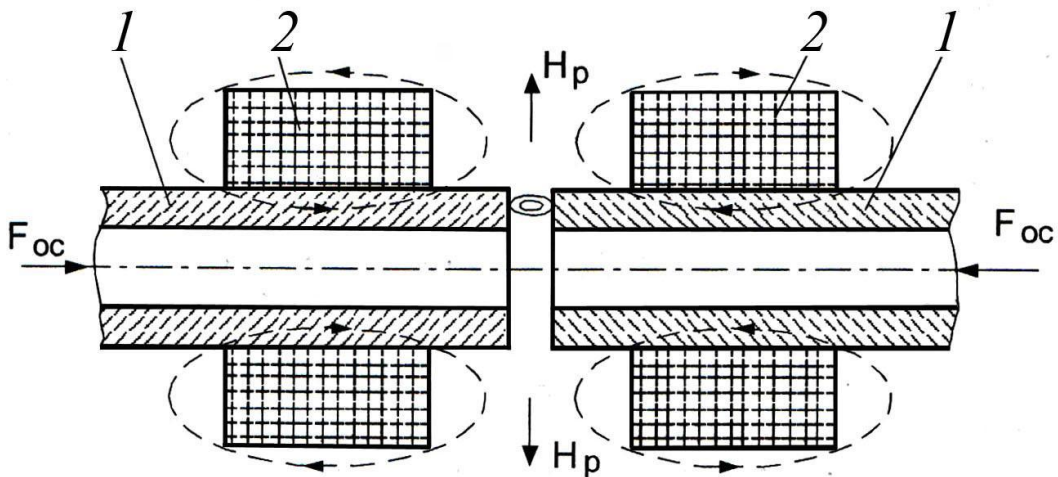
Схема дугоконтактного зварювання: 1 – зварювані деталі; 2 – котушки електромагнітів; $F_{ос}$ – зусилля осадження.
